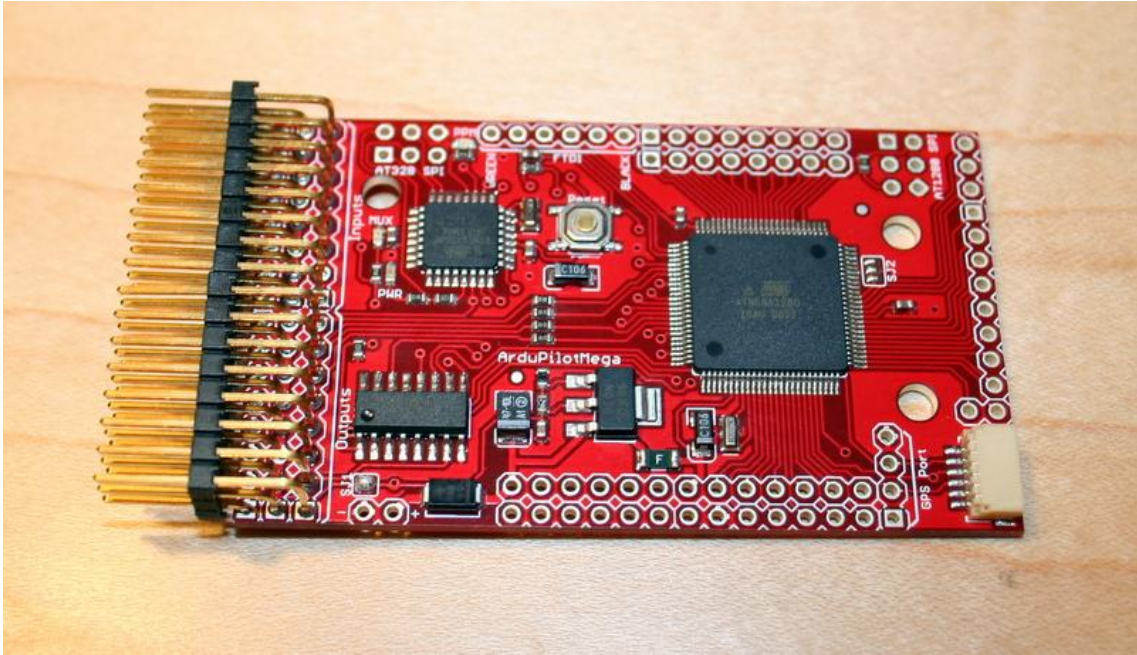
Placa Ardupilot amb els pin headers amb angle soldats.
